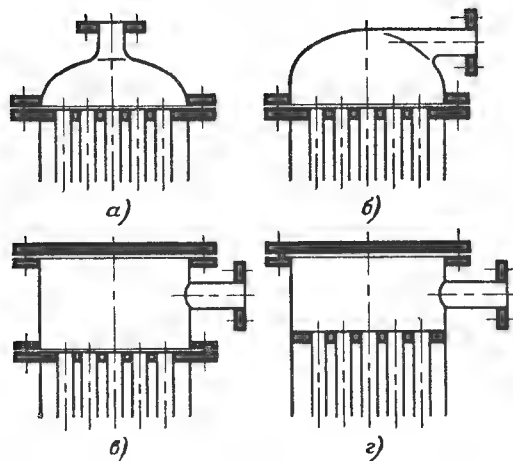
Типы соединений крышки с корпусом аппарата и трубопроводами.
